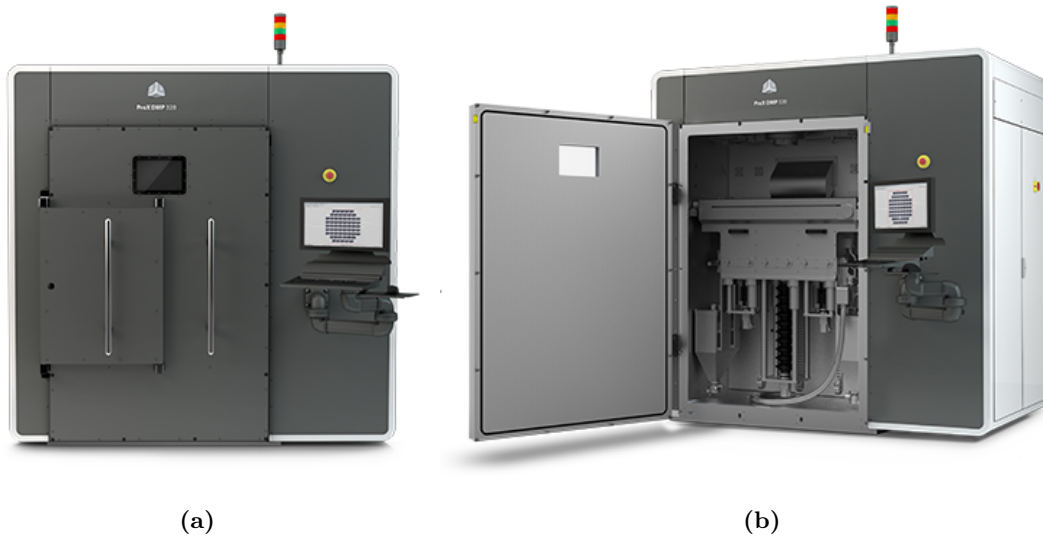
Visualisation de la machine 3D Systems ProX DMP 320 choisie pour l'élaboration de pièces à partir de poudre d'Inconel 625 (a) Vue avec porte fermée et (b) Vue avec porte ouverte sur la chambre de fabrication.
